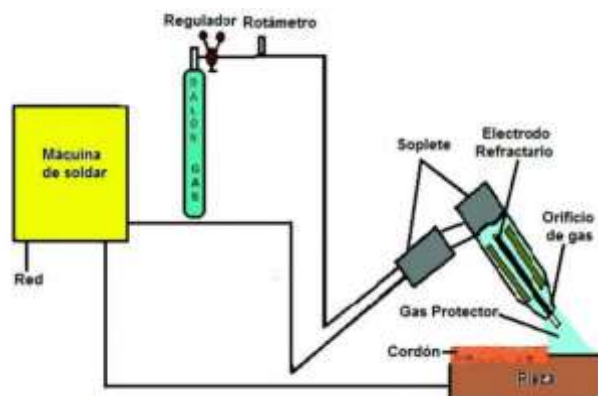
Esquema del proceso de soldadura TIG
